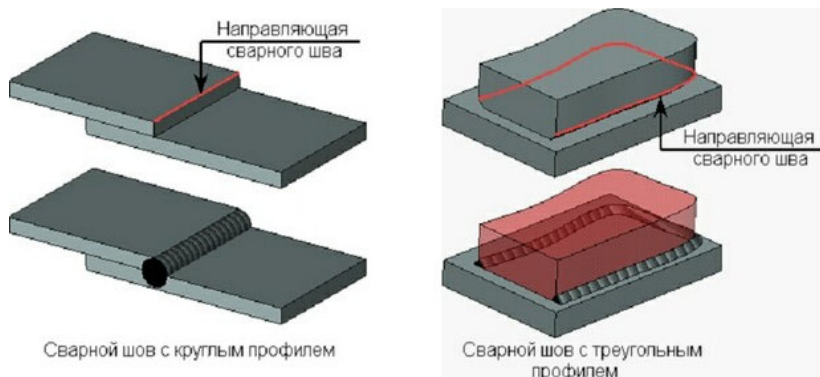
Примеры создания сварного шва по направляющей
